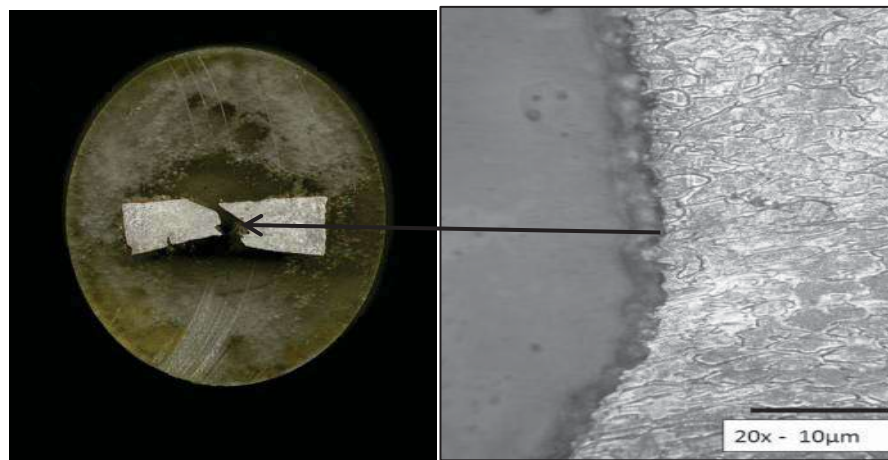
Vista longitudinal de la fractura dúctil en el cordón de soldadura después del ensayo de tensión.
